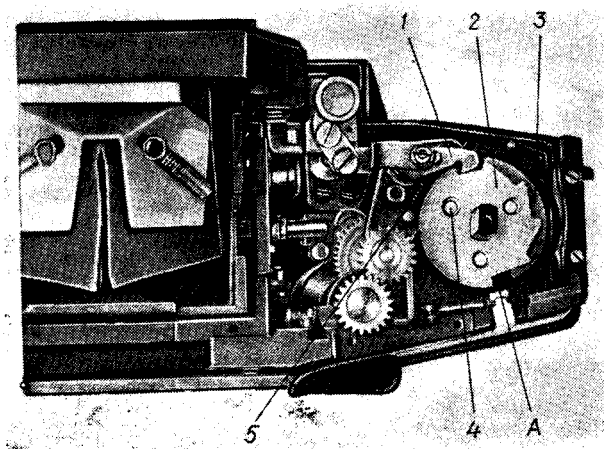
Фотоаппарат без верхней крышки, счетчика кадров, муфт и колеса зубчатого:
